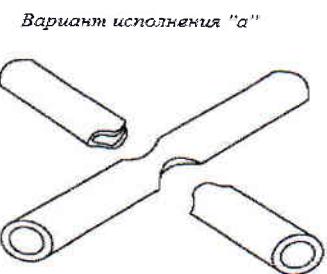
(а) Расположение отверстий при конструировании узла Б.
